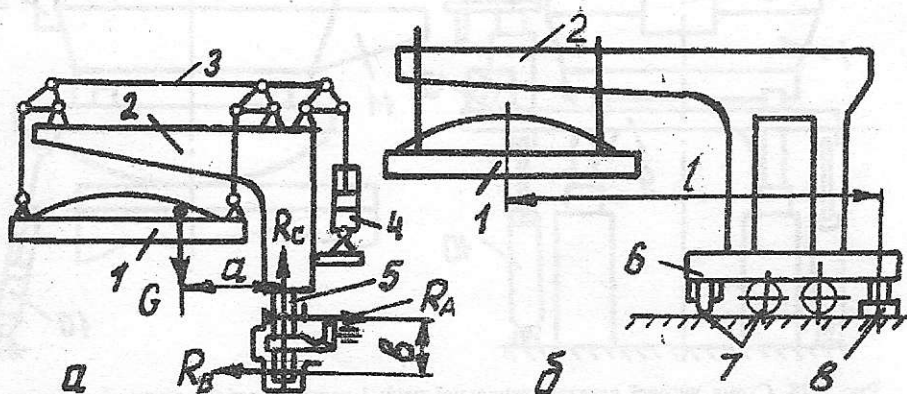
Схеми механізмів підйому і повороту свода з поворотною колоною (а) і платформою (б); 1-склепіння; 2-напівportal; 3-важильна система; 4-гідроциліндр; 5-поворотна колона; 6-платформа; 7-катки; 8-центрувальна вісь
